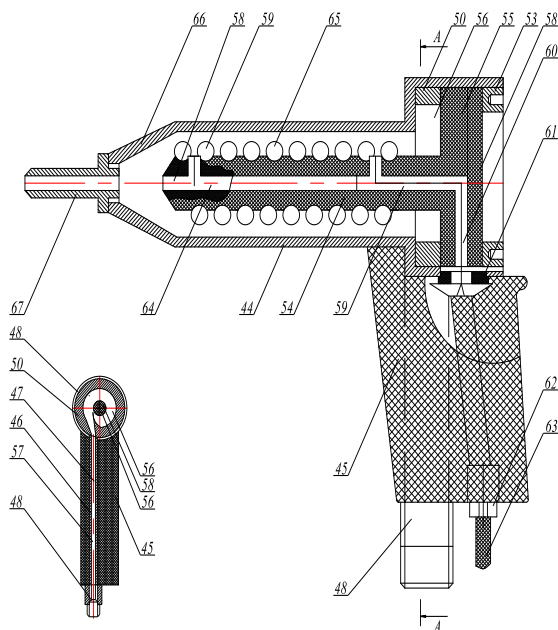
Пристрій для зварювання термопластів нагрітим газом
